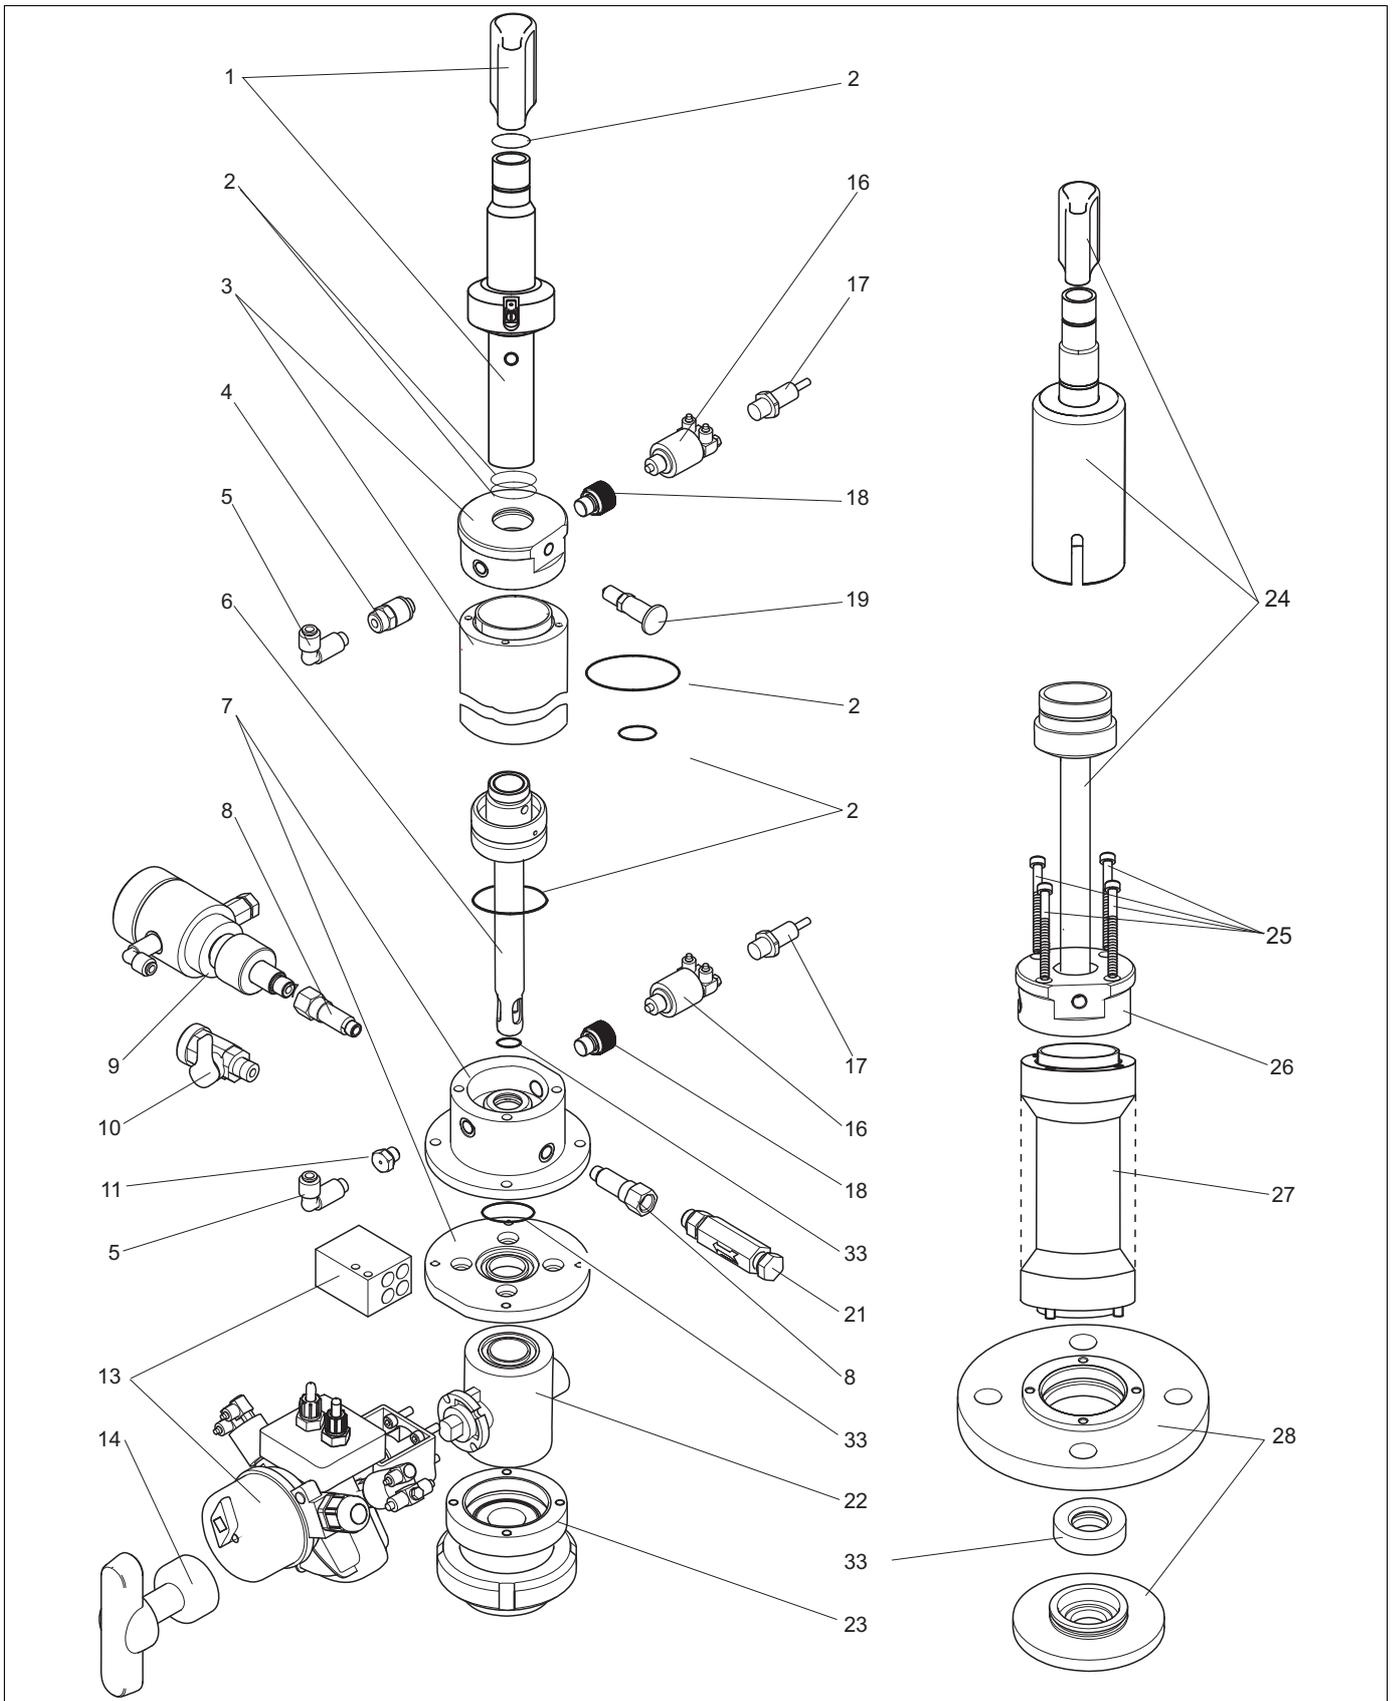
Ersatzteile (alle Armaturenausführungen)
